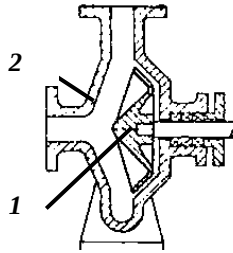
Схема радіального (відцентрового) нагнітача: 1 – робоче колесо; 2 – корпус; 3 – всмоктувальний патрубок; 4 – напірний патрубок
